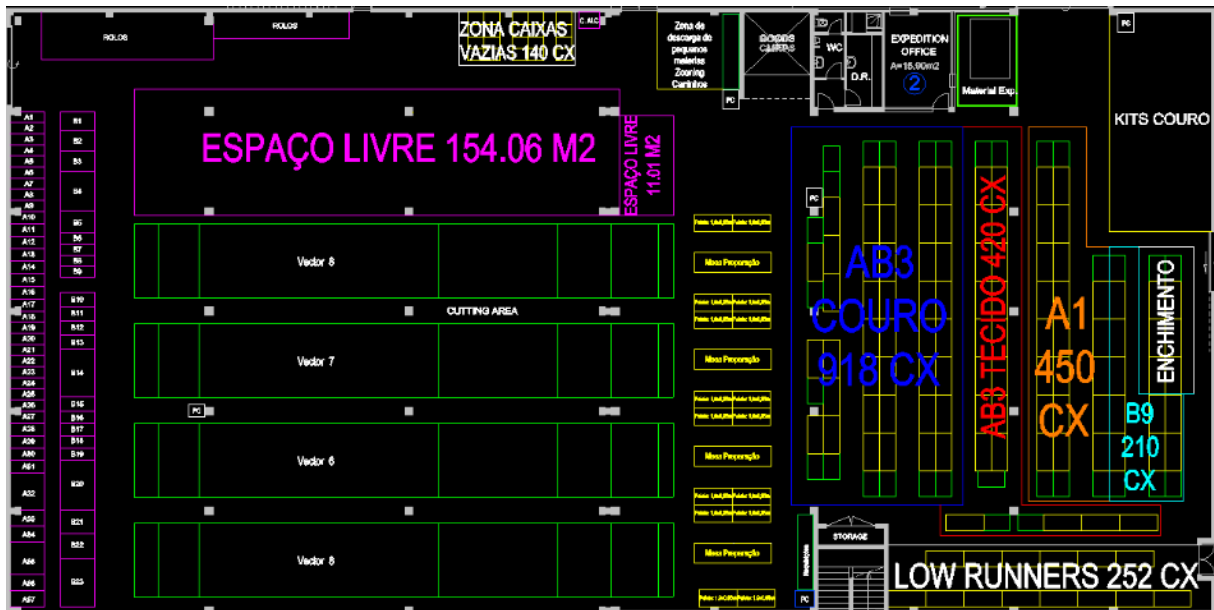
Terceira proposta layout futuro secção corte Joane I
